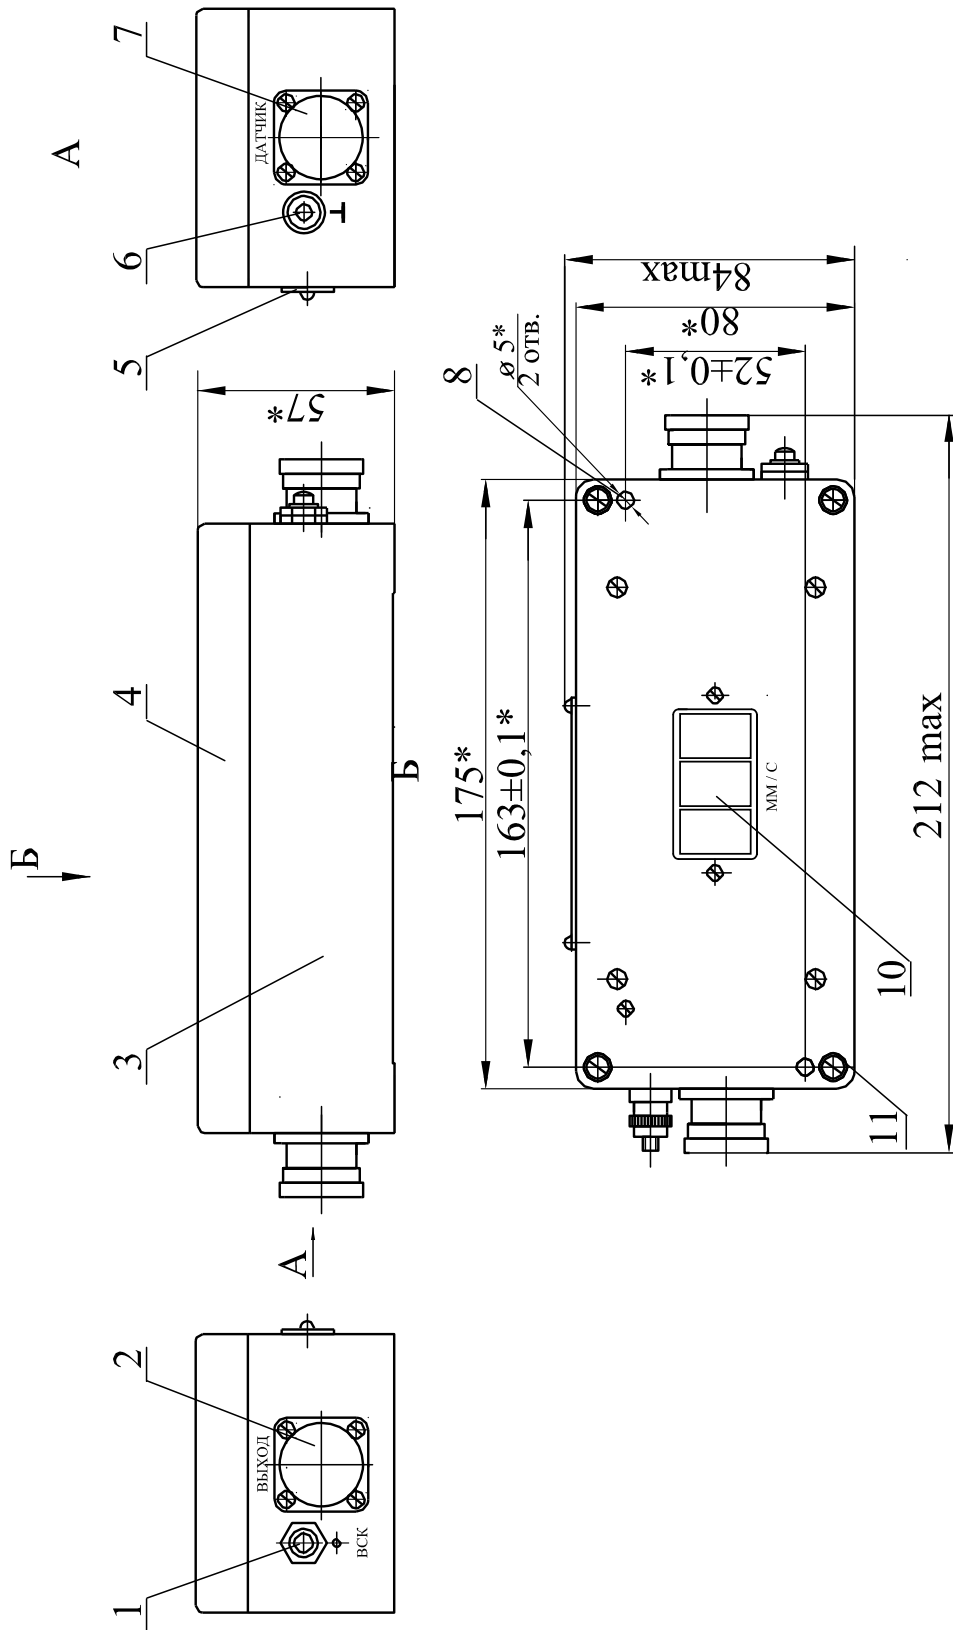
(1 из 2) - Габаритно - установочные размеры блока БЭ-38-30
